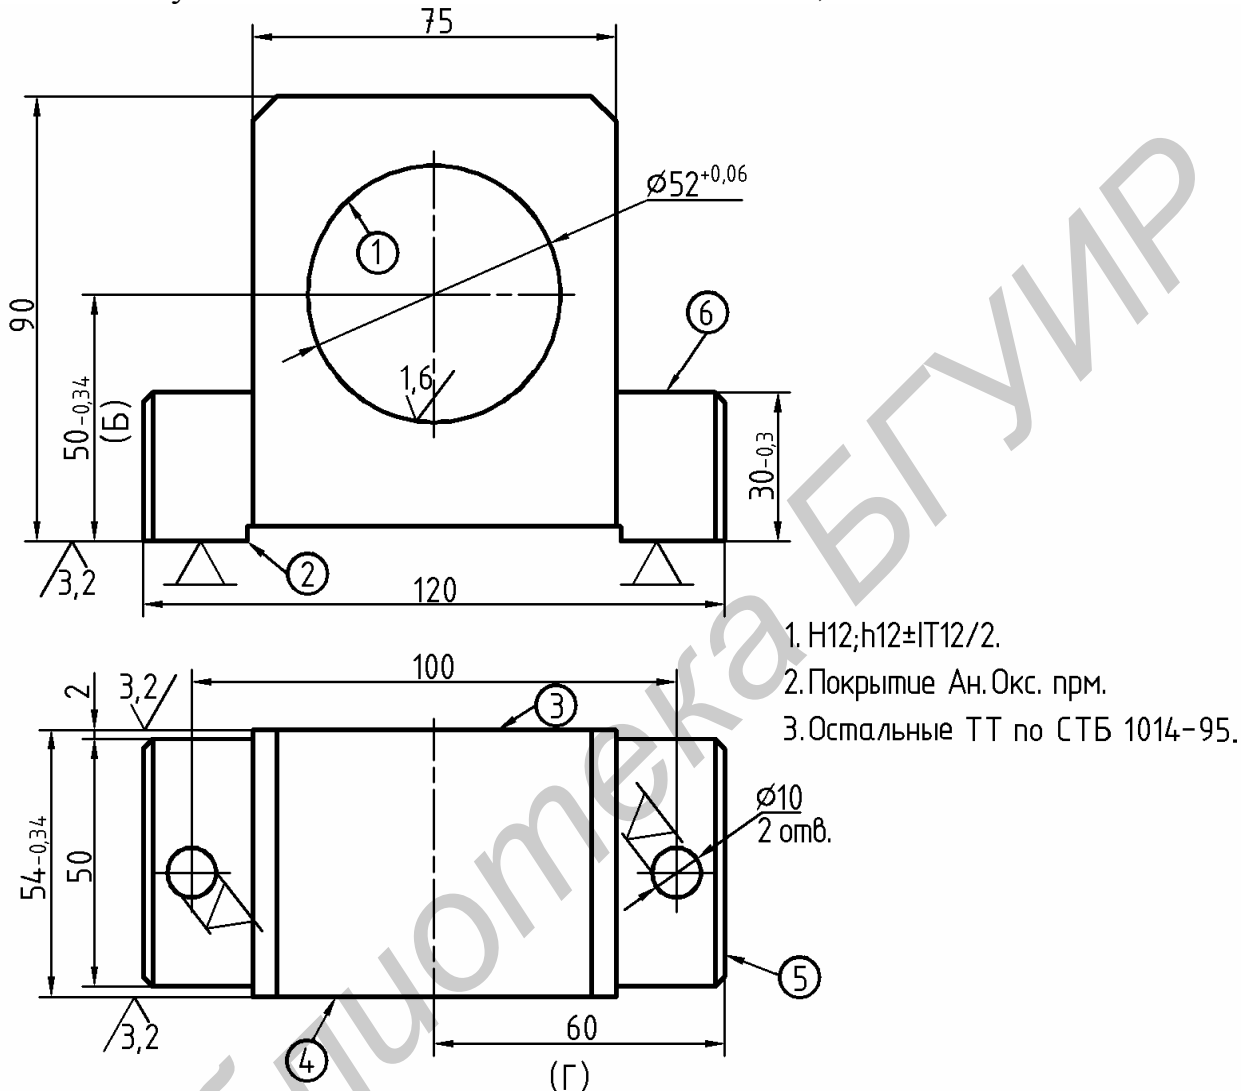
Корпус подшипника: чертеж и схема установки при обработке отверстия $\varnothing 52^{+0.06}$ мм
